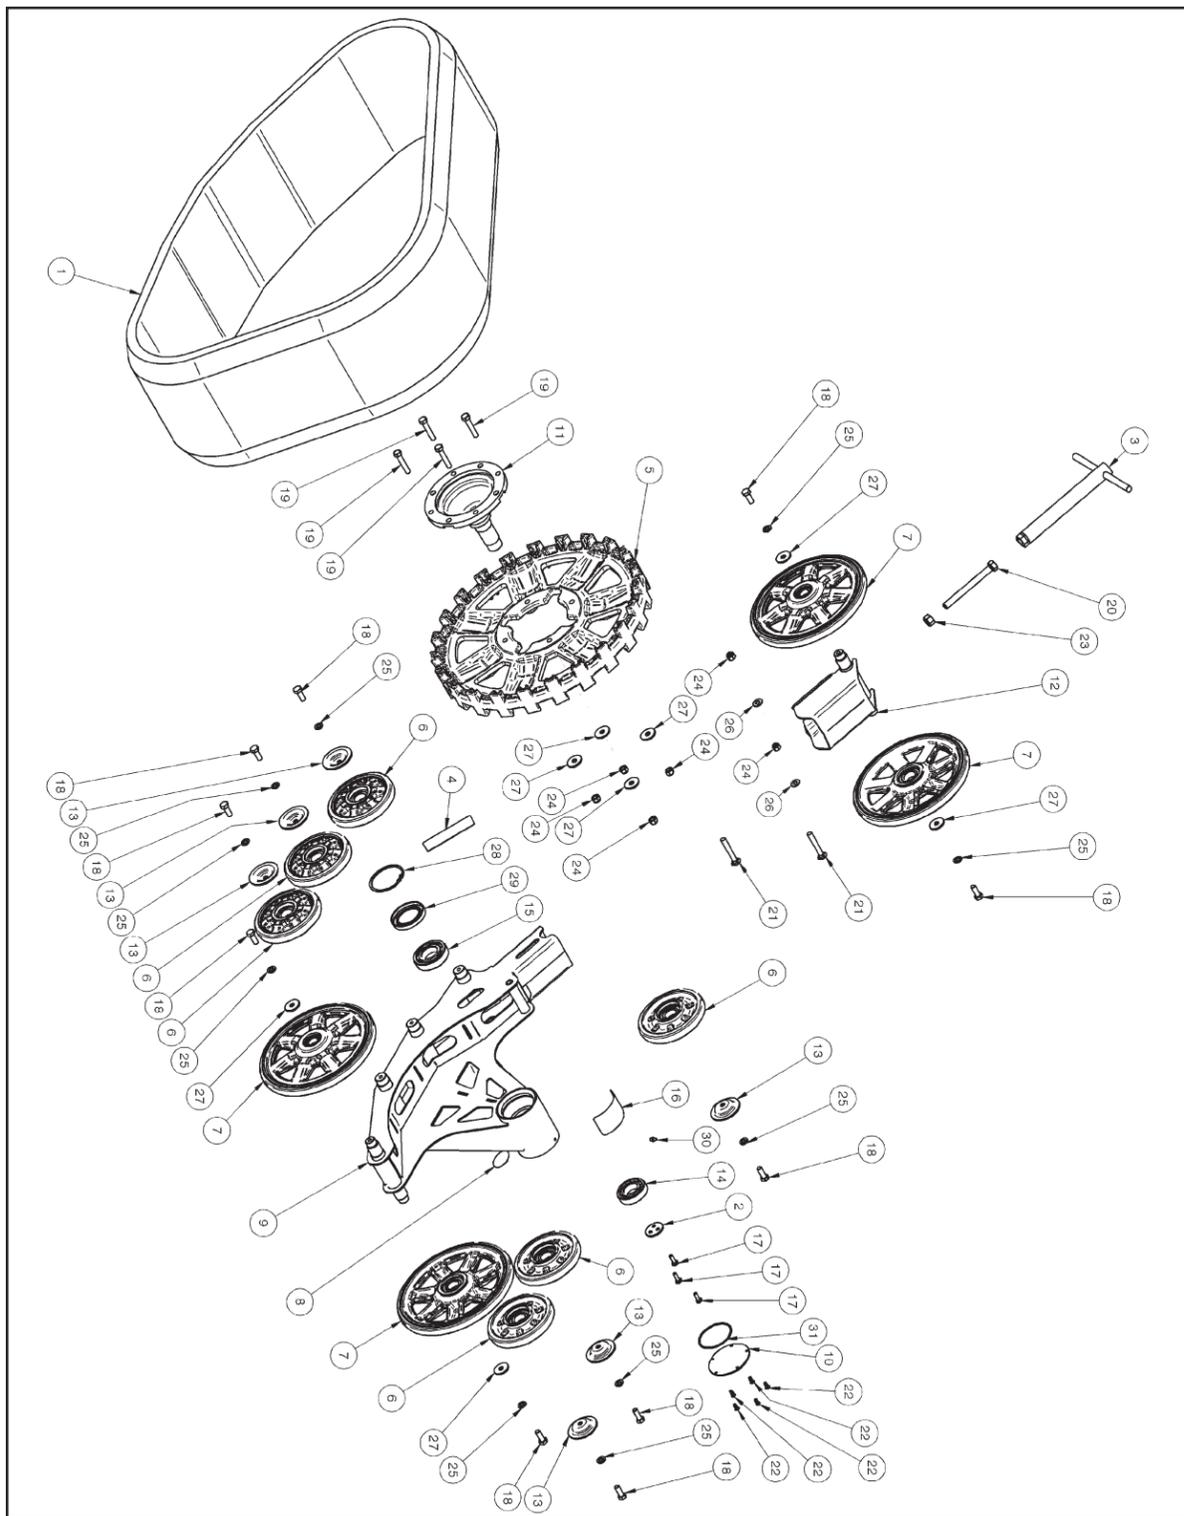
Vue explosée - Ensemble de chenille avant droit
